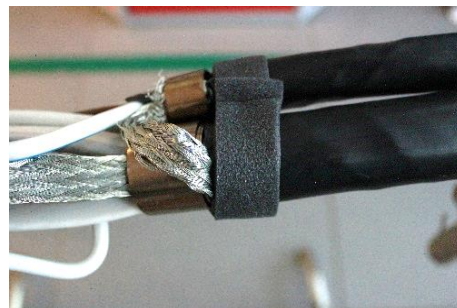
Установка поводка заземления и губчатых уплотнителей для герметизации
